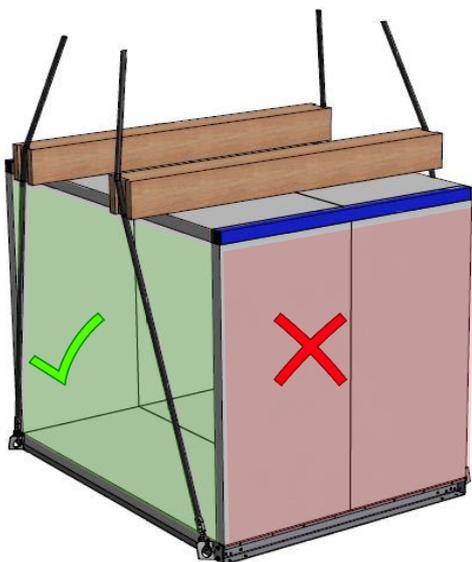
Far passare gli elementi di sospensione dal lato frontale
